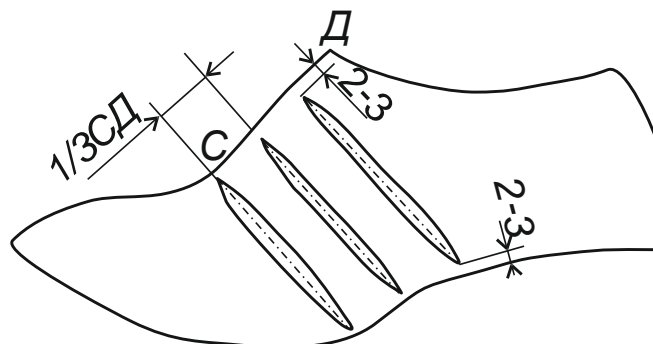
Розтин зліпку бокової поверхні колодки
